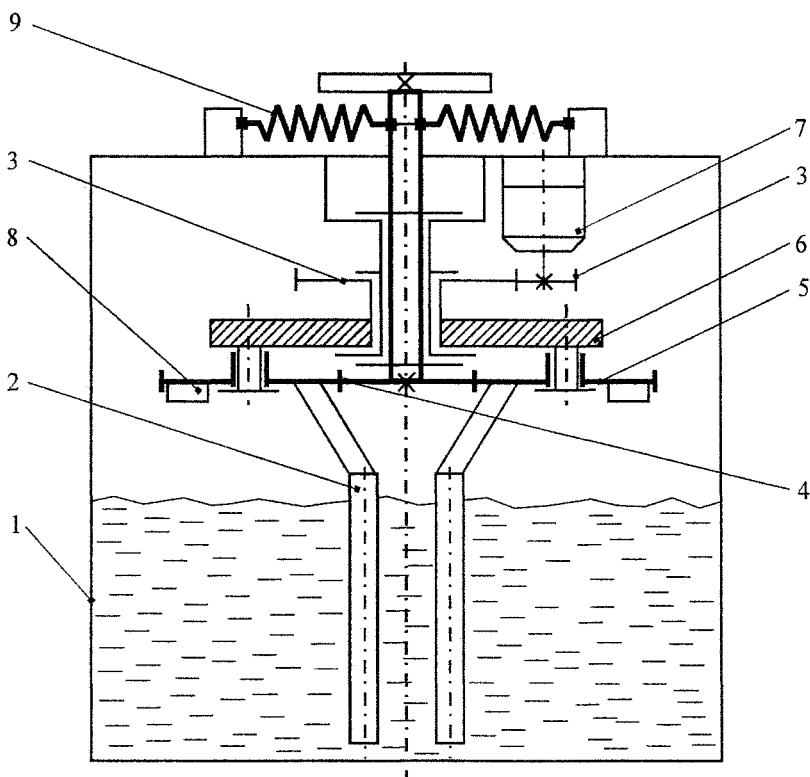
Схема планетарного привода смесителя с центральным упругим элементом: 1 – корпус; 2 – рабочий орган; 3 – передаточный механизм; 4 – центральная шестерня; 5 – сателлиты; 6 – водило; 7 – двигатель; 8 – противовесы; 9 – упругий элемент
